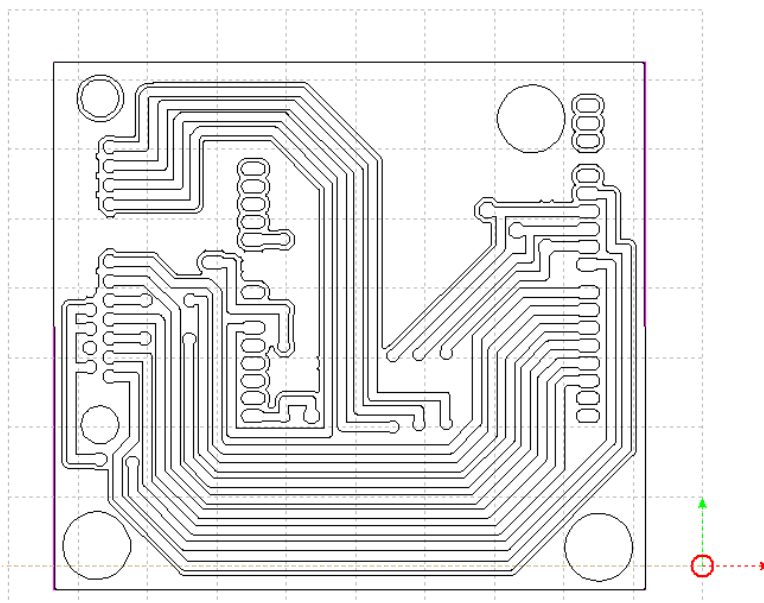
visualización de la capa Bottom de la PCB en el software bCNC
